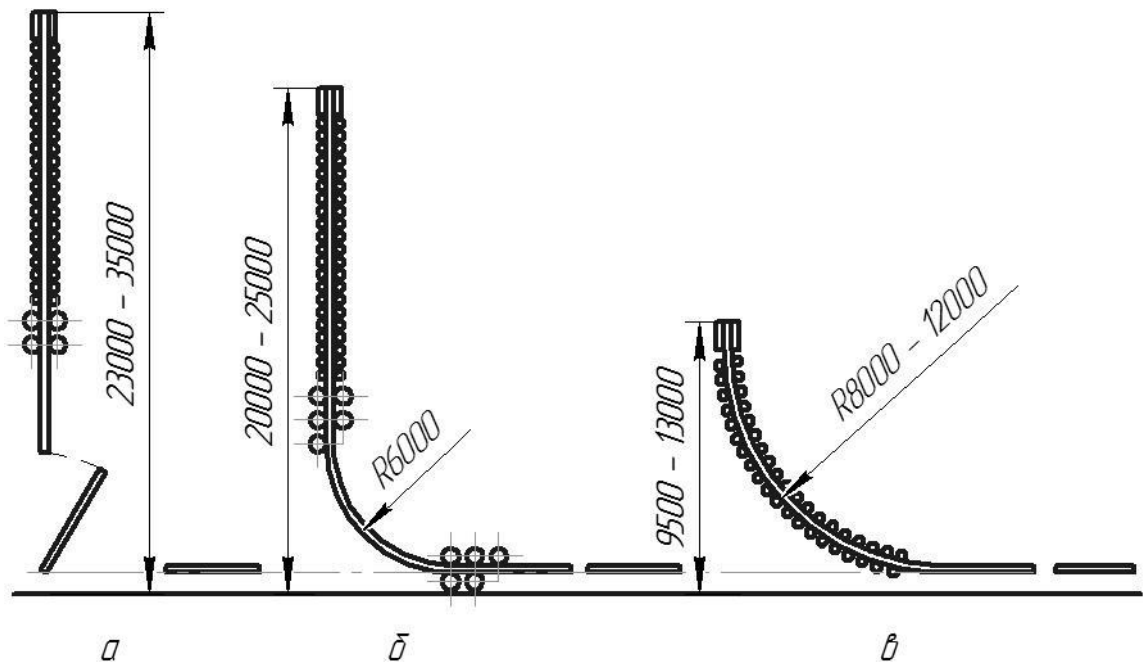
Схем машин безперервного лиття заготовок:
